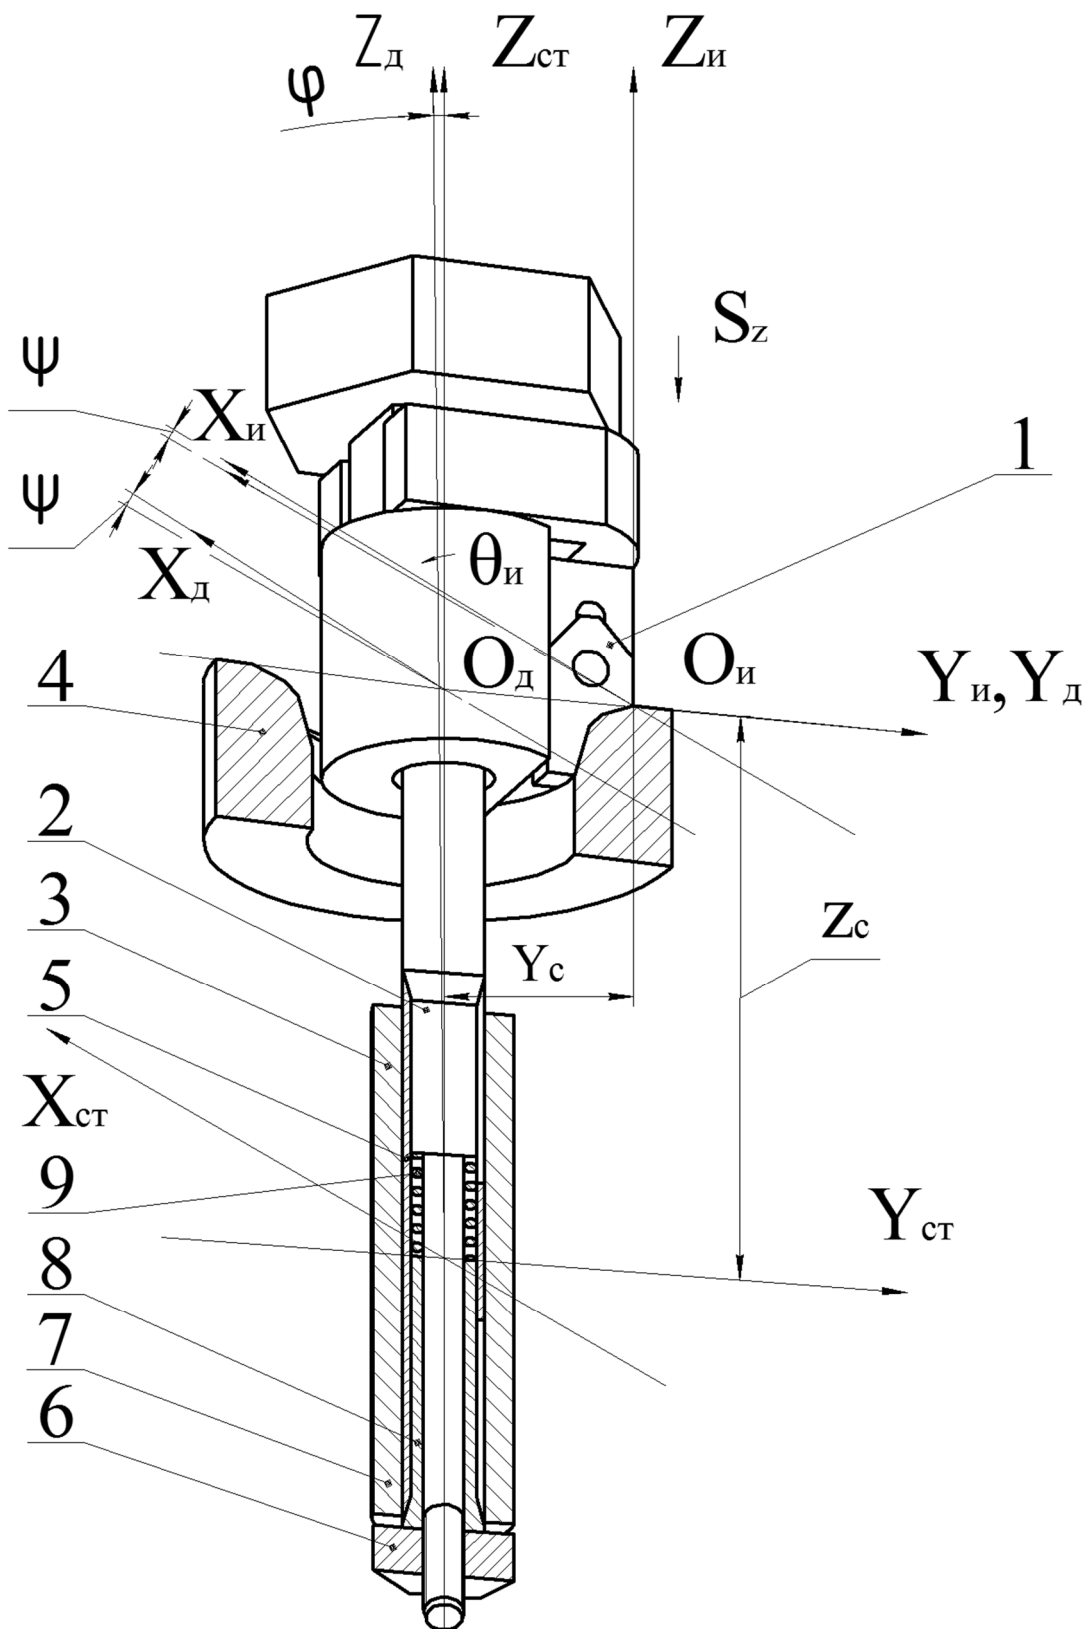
Схема растачивания рабочей поверхности седла клапана
